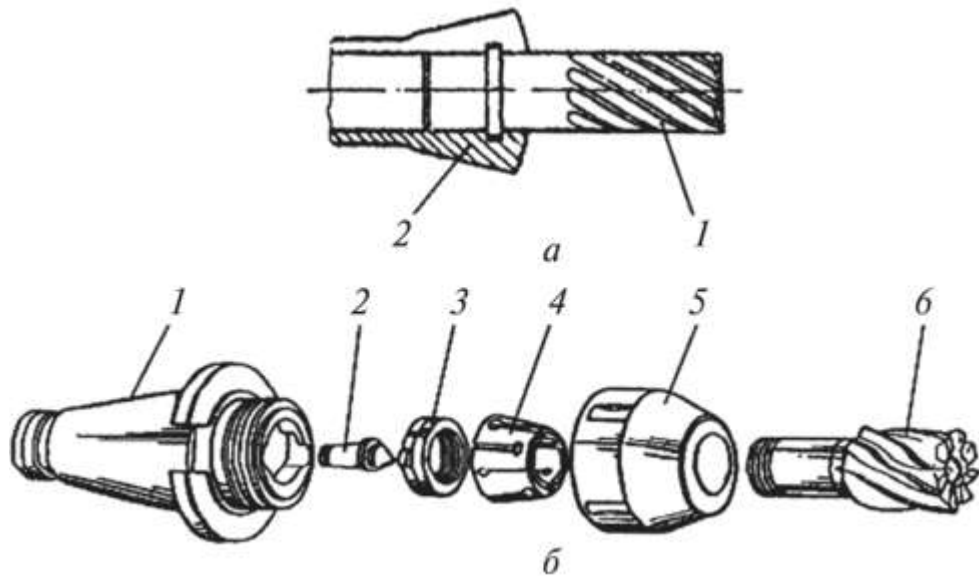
Схема закріплення кінцевої фрези з буртиком (а) та з різьбленням (б) у цанговому патроні: а: 1 - фреза; 2 - цанга; б: 1 - патрон; 2 - центр; 3 - кільце; 4 - цанга; 5 - накидна гайка; 6 - фреза
